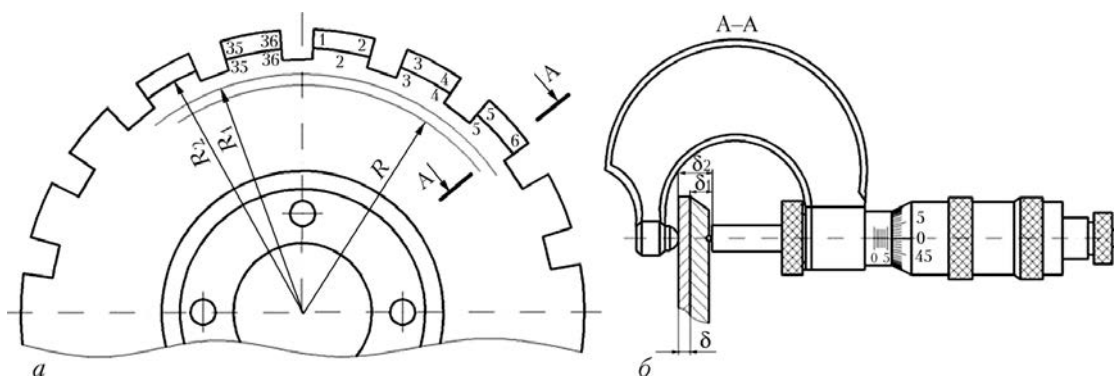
Схема конфигурации ножа-ботвореза свеклоуборочного комбайна (а), сечение ножа по А–А с устройством для замера толщины наплавленного слоя (б)
